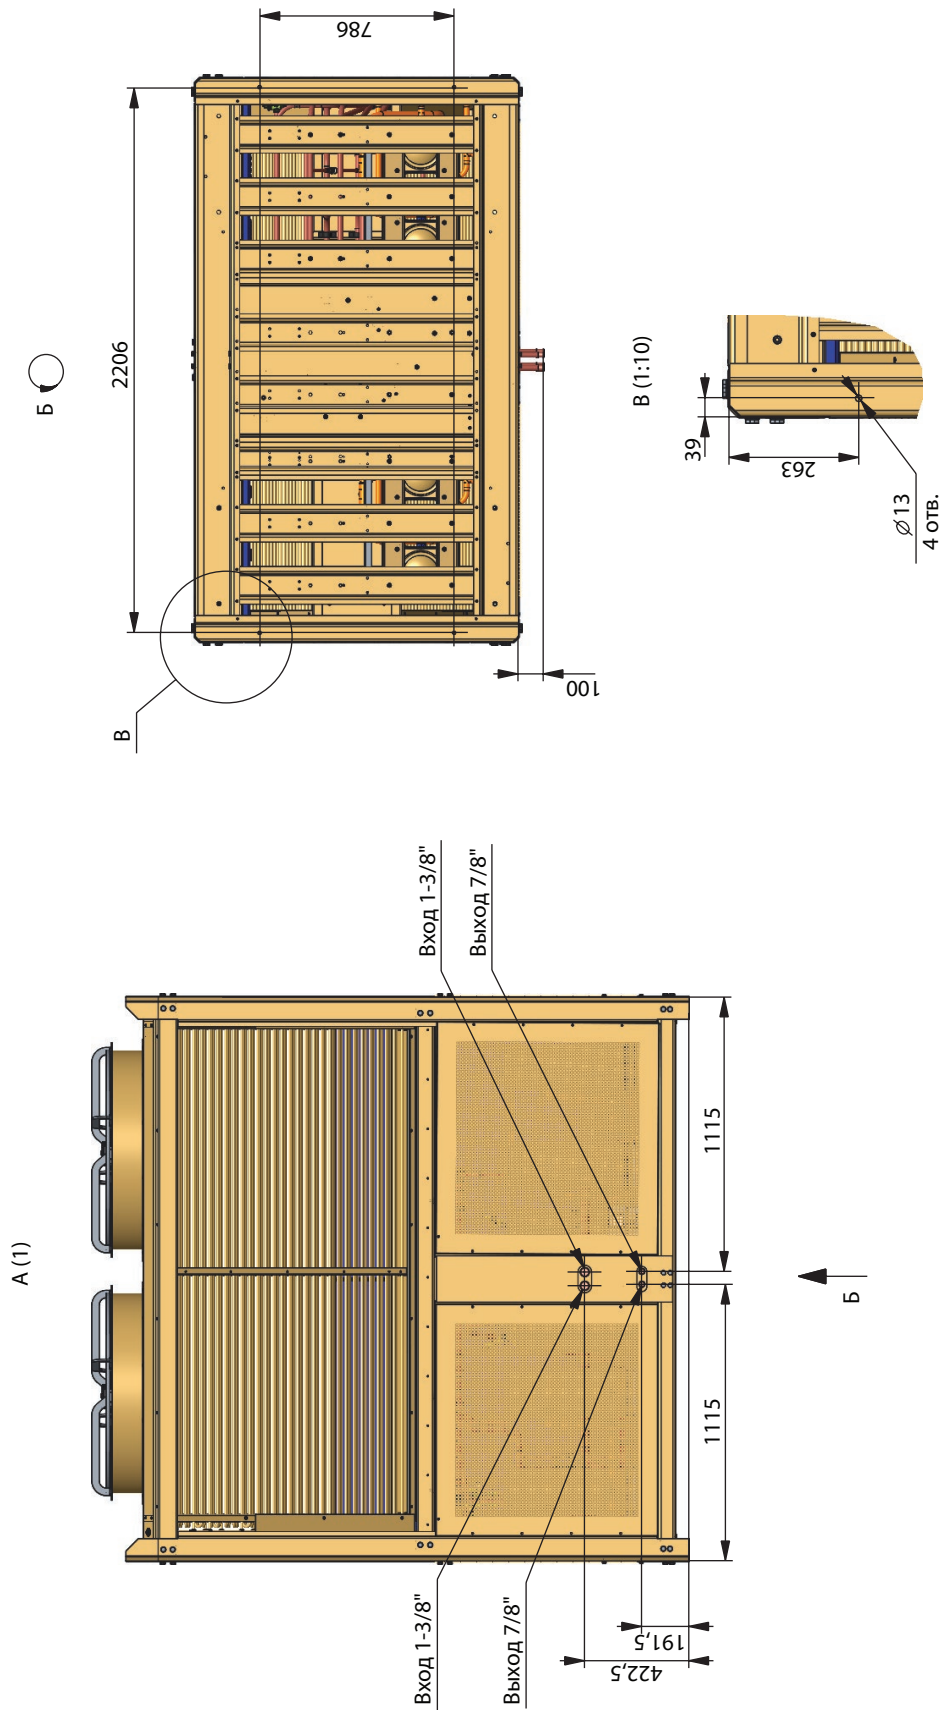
Агрегат компрессорный типа МАКК 330-1202, -1402, -1602
